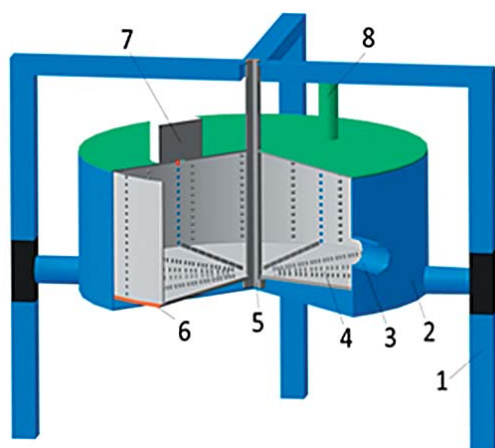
Установка с вращающимся цилиндрическим резонатором в виде тёрки
